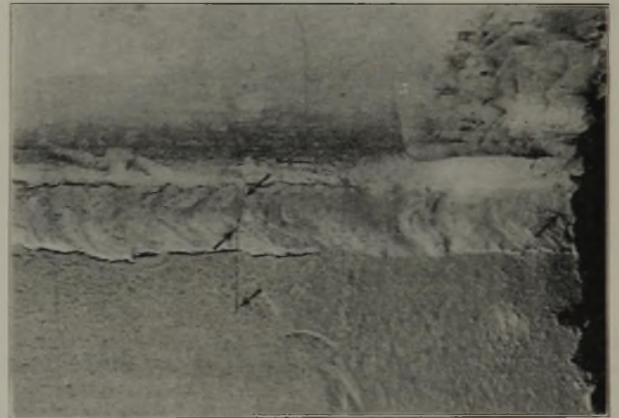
Ribstelle parallel zur Schweißnaht magnetisch durchflutet; Rückseite.
